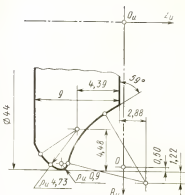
Профиль дисковой фрезы для обработки винтовых канавок у цилиндрической фрезы
